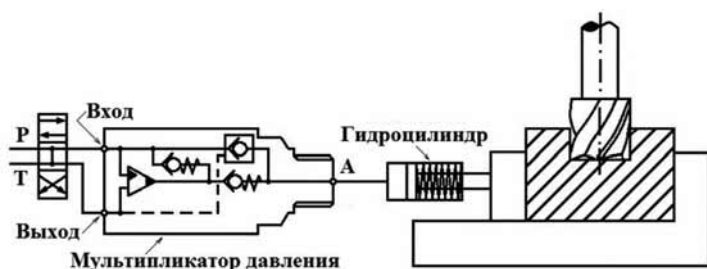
Схема мультипликатора давления в приводе зажимного устройства станка
